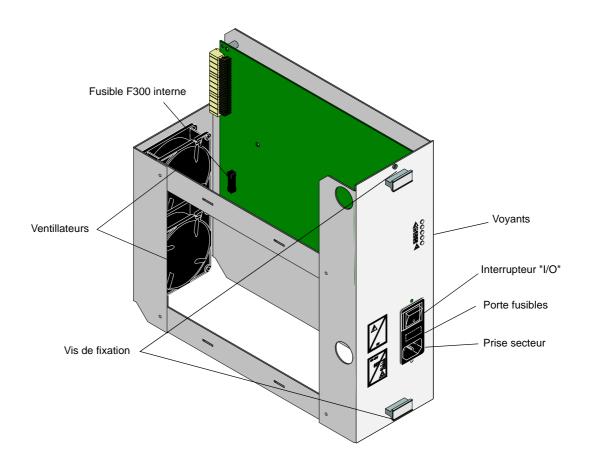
VUE D'ENSEMBLE DU MODULE ADS300 XD
